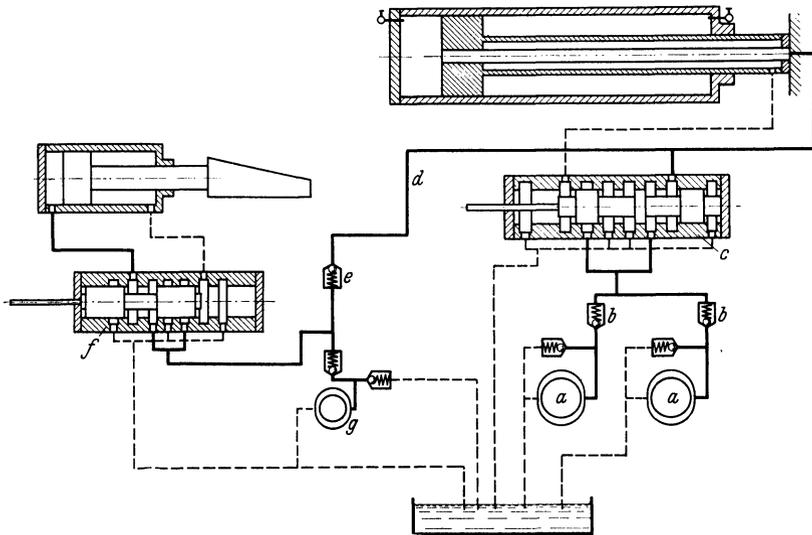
Ölkreislauf einer Zylinderblockräummaschine mit Tischbewegung.
